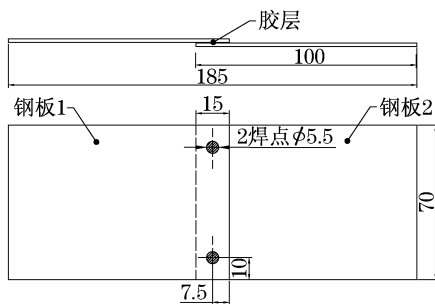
胶焊接头形状与尺寸(单位:mm)
